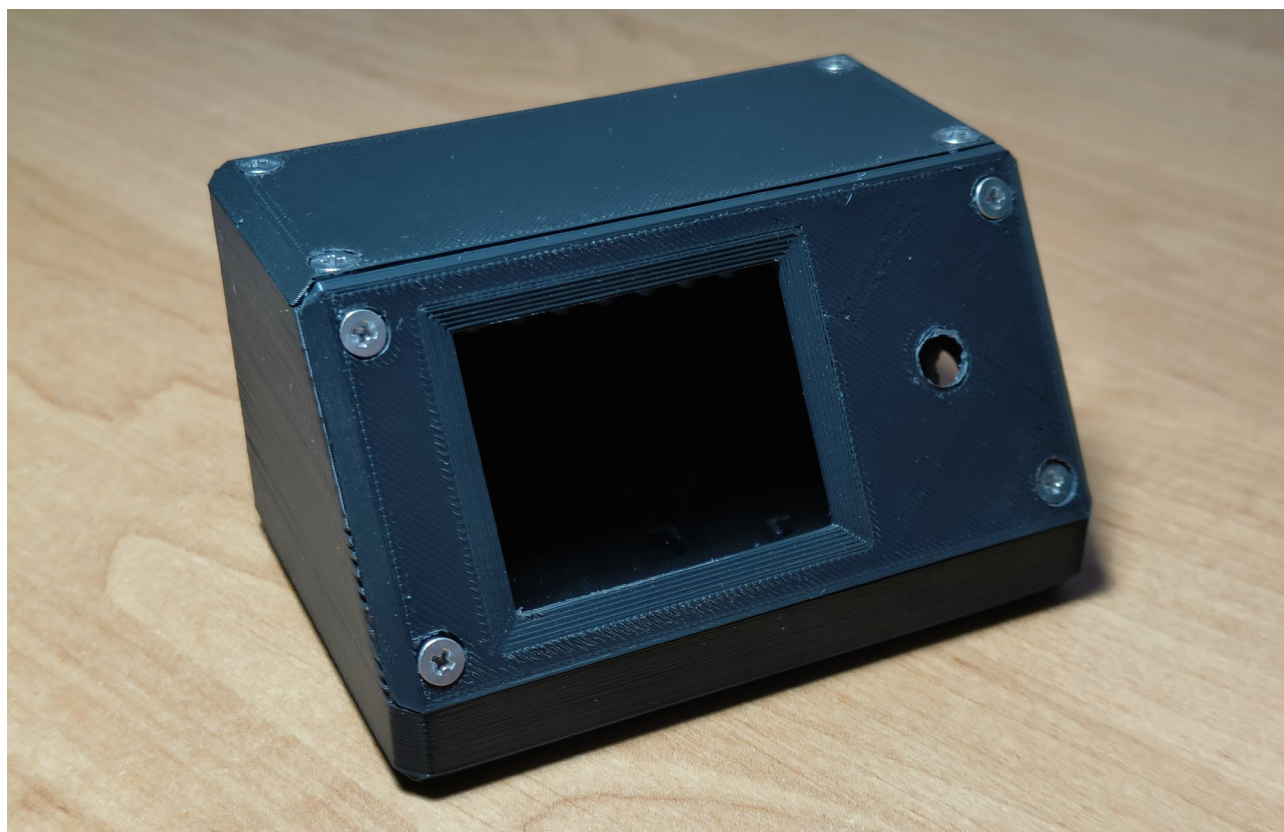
Загальний вигляд виготовленого корпусу після 3D-друку
